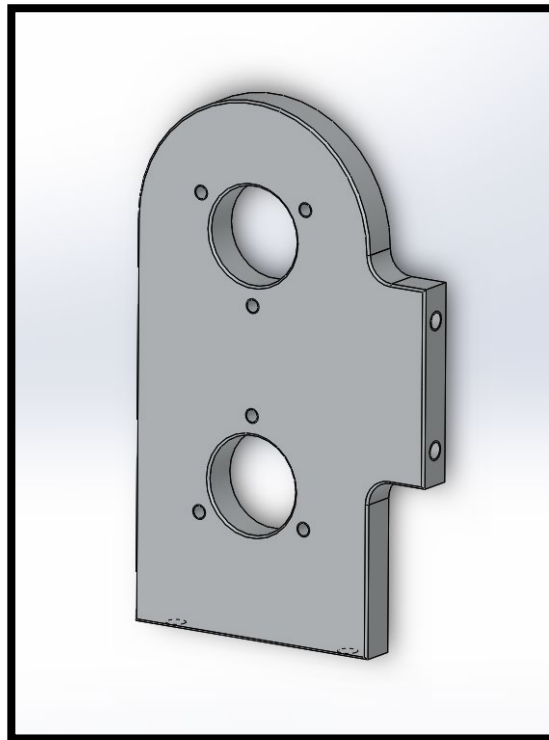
Isométrico de la pieza soporte del cigüeñal
